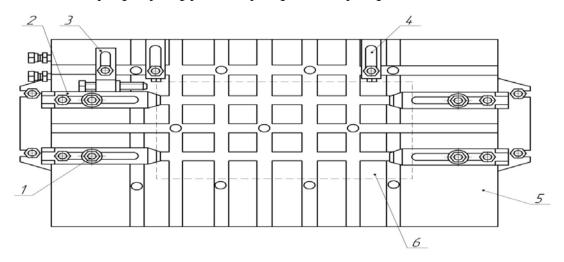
Универсально-наладочное приспособление для установки корпусных деталей: 1 — шпилька; 2 — прихват; 3 — упор; 4 — регулируемый упор; 5 — плита; 6 — заготовка
